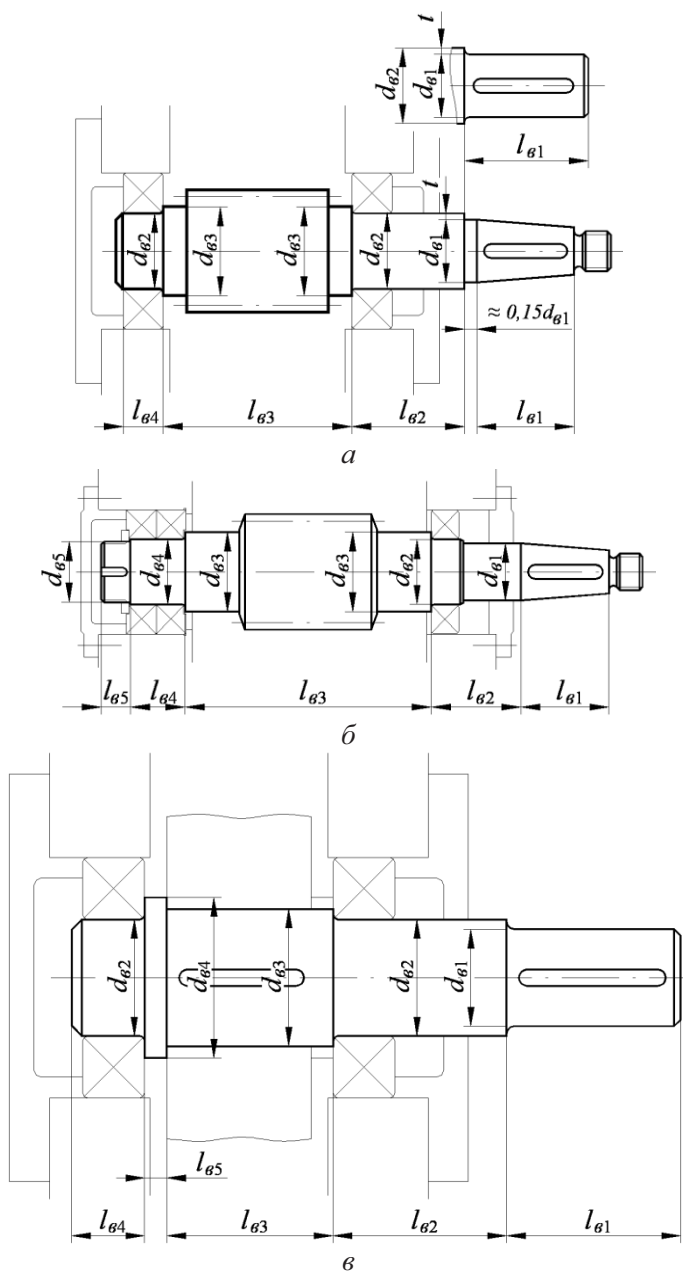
Типовые конструкции валов одноступенчатых редукторов
